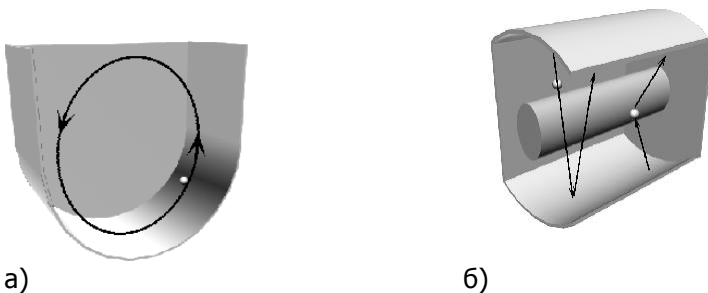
Схема движения инденторов обрабатываемой среды в камерах с циркуляцией по эллипсу (а) и возвратно-поступательным движением (б)
